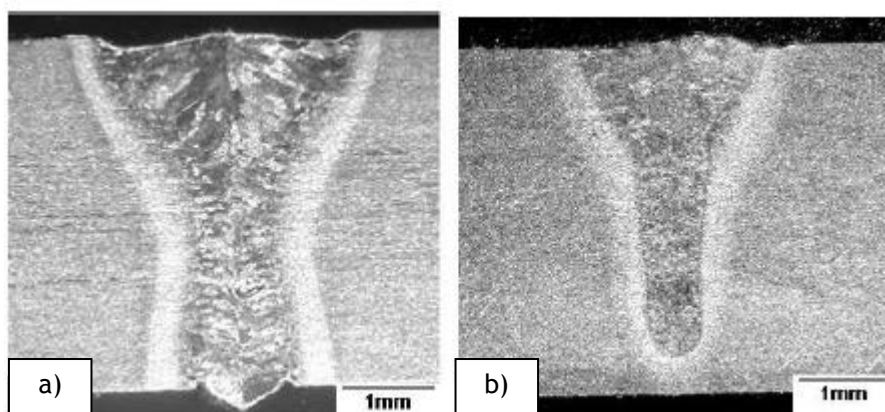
Macrografia da secção transversal de um cordão obtido por laser em placas de Ti-6Al-4V com 4mm de espessura, utilizando diferentes velocidades de soldadura: a) 4mm/min; b) 6mm/min
